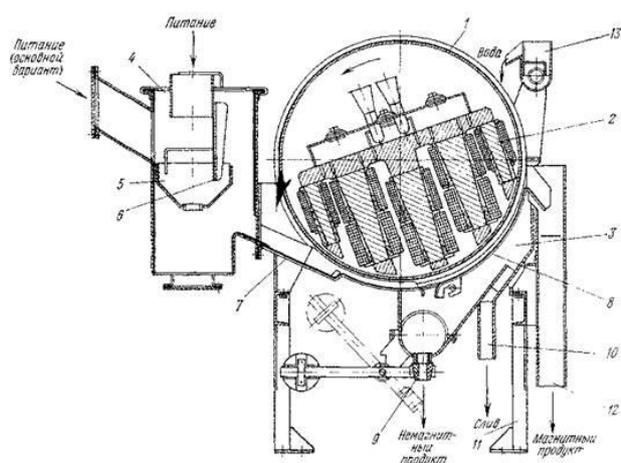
Схема сепаратора ПБМ-90/250: 1 – барабан; 2 – магнитная система; 3 – ванна; 4, 12 – загрузочная и разгрузочная коробки; 5 – распределительная коробка; 6 – успокоитель; 7 – питающий лоток; 8 – концентратный лоток; 9 – хвостовые насадки; 10 – сливной патрубок; 11 – рама; 13 – брызгало
